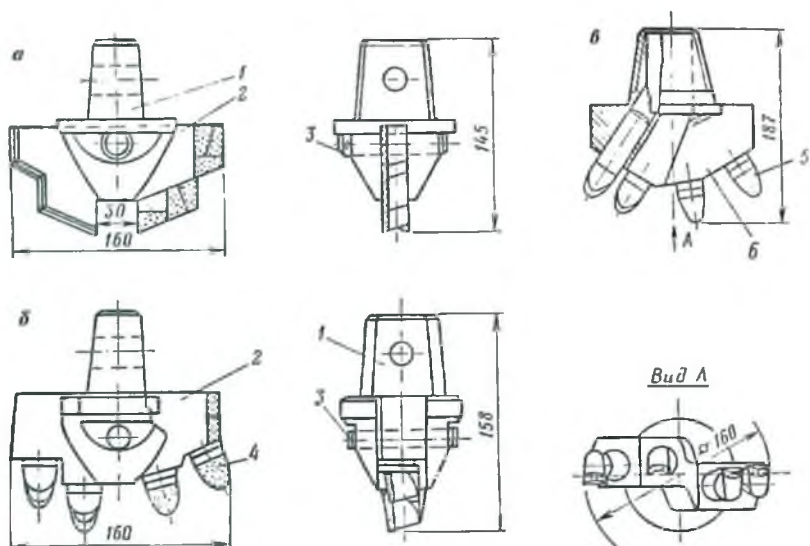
Режущие долота для бурения со шнековой очисткой скважин: а — РК4М, б — ВРД160Ш; в — 10РД160ШП; 1 — хвостовик; 2 — съемный корпус; 3 — дополнительный палец; 4, 5 — резец типа ШБМ2С укороченный; 6 — литой корпус
